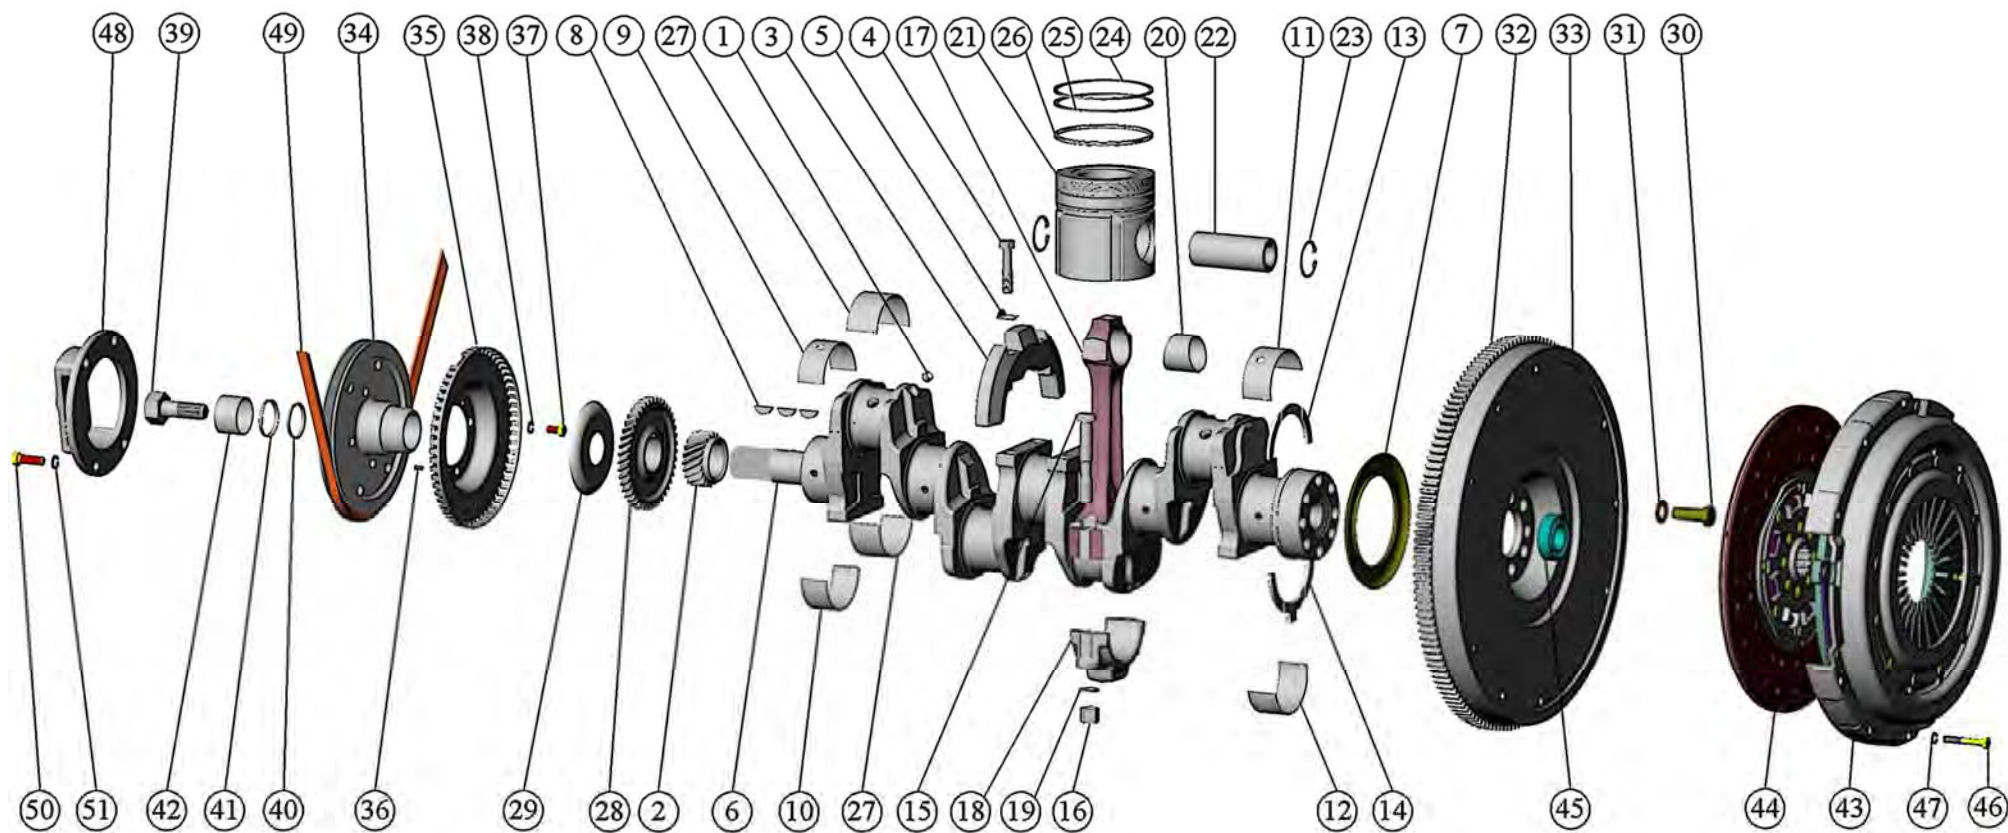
Установка поршневой группы. Вал коленчатый и маховик. Установка муфты сцепления.
